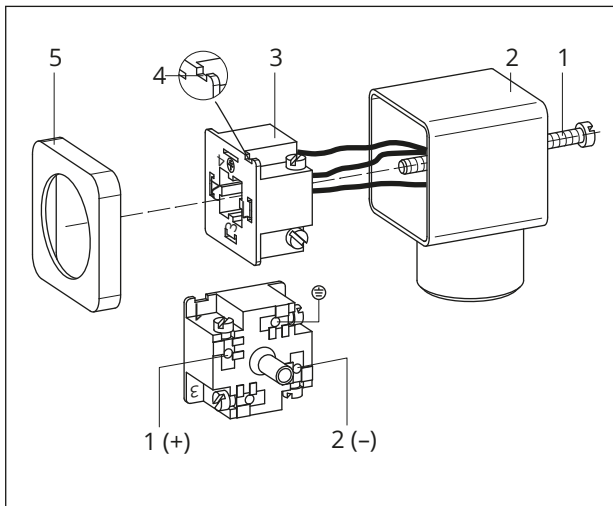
Klemmenanschluss (Eingangssignal · Typ 6111)
